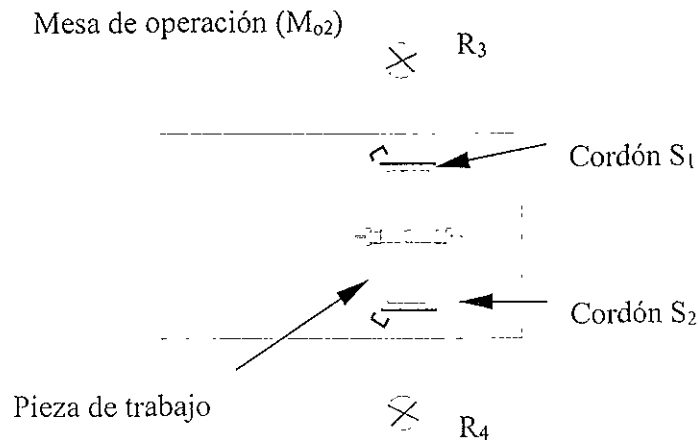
Robots Industriales para el proceso de soldadura.
